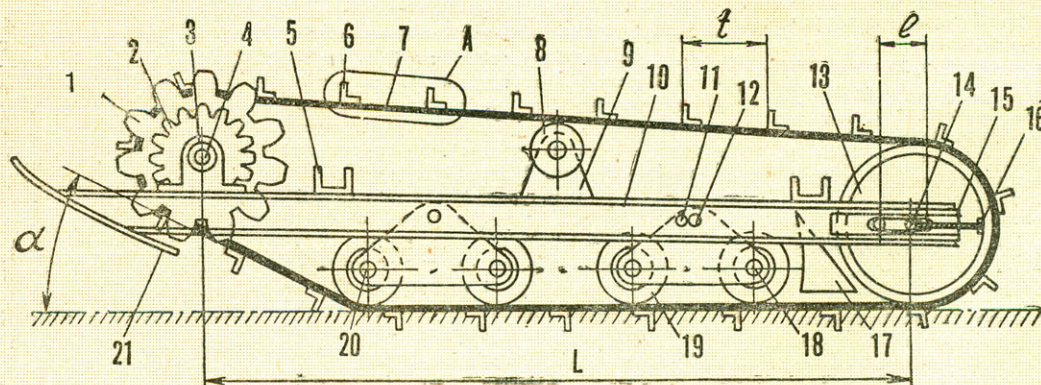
Конструктивная схема гусеничного движителя мотонарт: 1 — ведущее колесо-барабан, 2 — ведущая звездочка, 3 — кронштейн ведущего вала, 4 — ведущая ось, 5 — поперечный швеллер каретки, 6 — грунтозацепы, 7 — гусеничная лента, 8 — поддерживающий ролик, 9 — кронштейн, 10 — продольный швеллер каретки, 11 — каретка опорных катков, 12 — ось каретки опорных катков, 13 — ведомое колесо-барабан, 14 — подвижная ось ведомого колеса-барабана, 15 — ползун натяжного механизма, 16 — натяжной болт, 17 — снегоотбойник, 18 — ось опорного катка (короткая), 19 — опорные катки, 20 — ось опорных катков, 21 — снегоуплотнитель;  $\alpha$  — угол встречи ленты со снегом,  $L$  — база,  $t$  — величина хода натяжного механизма,  $e$  — шаг грунтозацепов.
